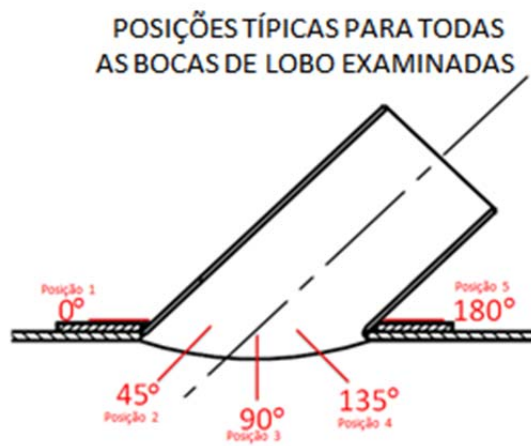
posições onde foram extraídos moldes da solda e simulados os feixes sônicos
